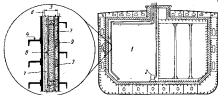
Схематический поперечный разрез газозара «Methane Princess».
